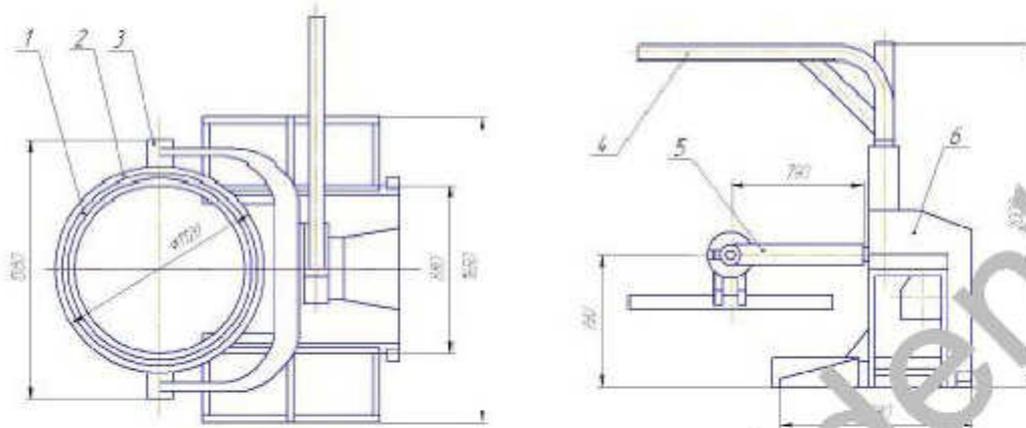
Стенд для разборки и сборки V-образных двигателей (Модель 6501-72)
